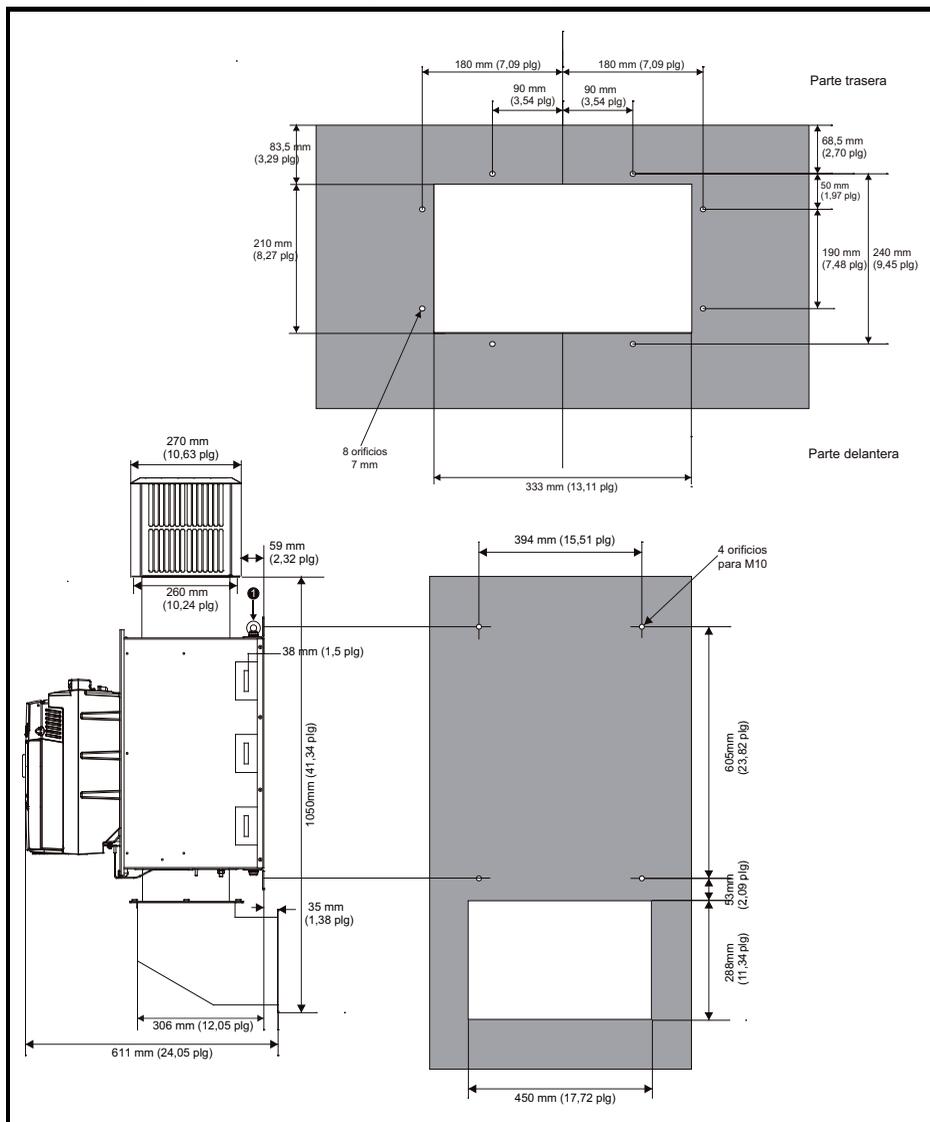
Placa posterior y detalles de montaje de los accionamientos de tamaño 2C
